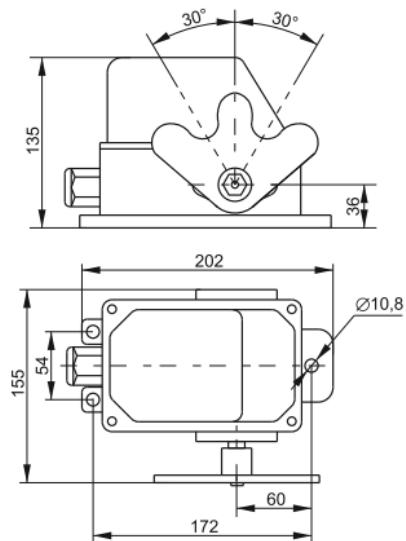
Габаритные и установочные размеры выключателей КУ-704 У1
